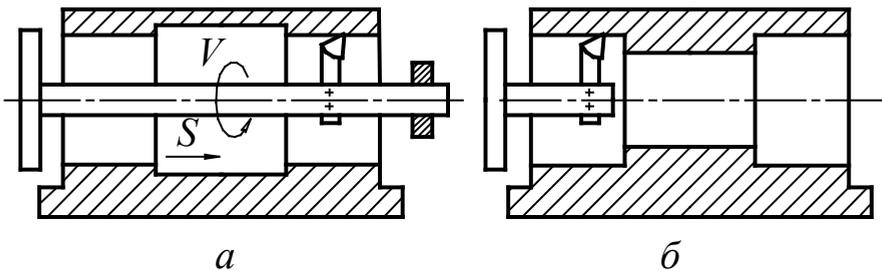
Конструкция корпусных деталей с соосными отверстиями:
